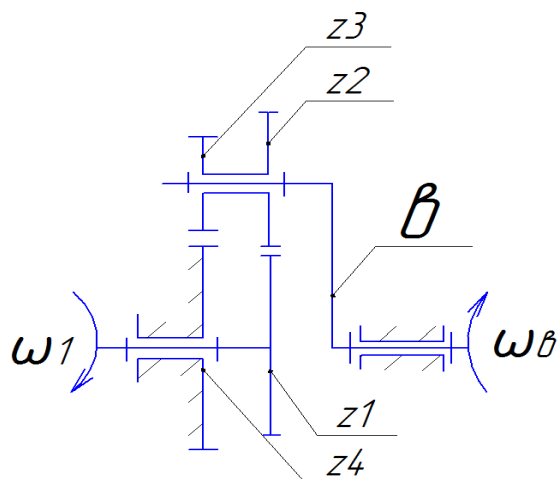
Структурная схема двухрядного планетарного редуктора с двумя внешними зацеплениями
